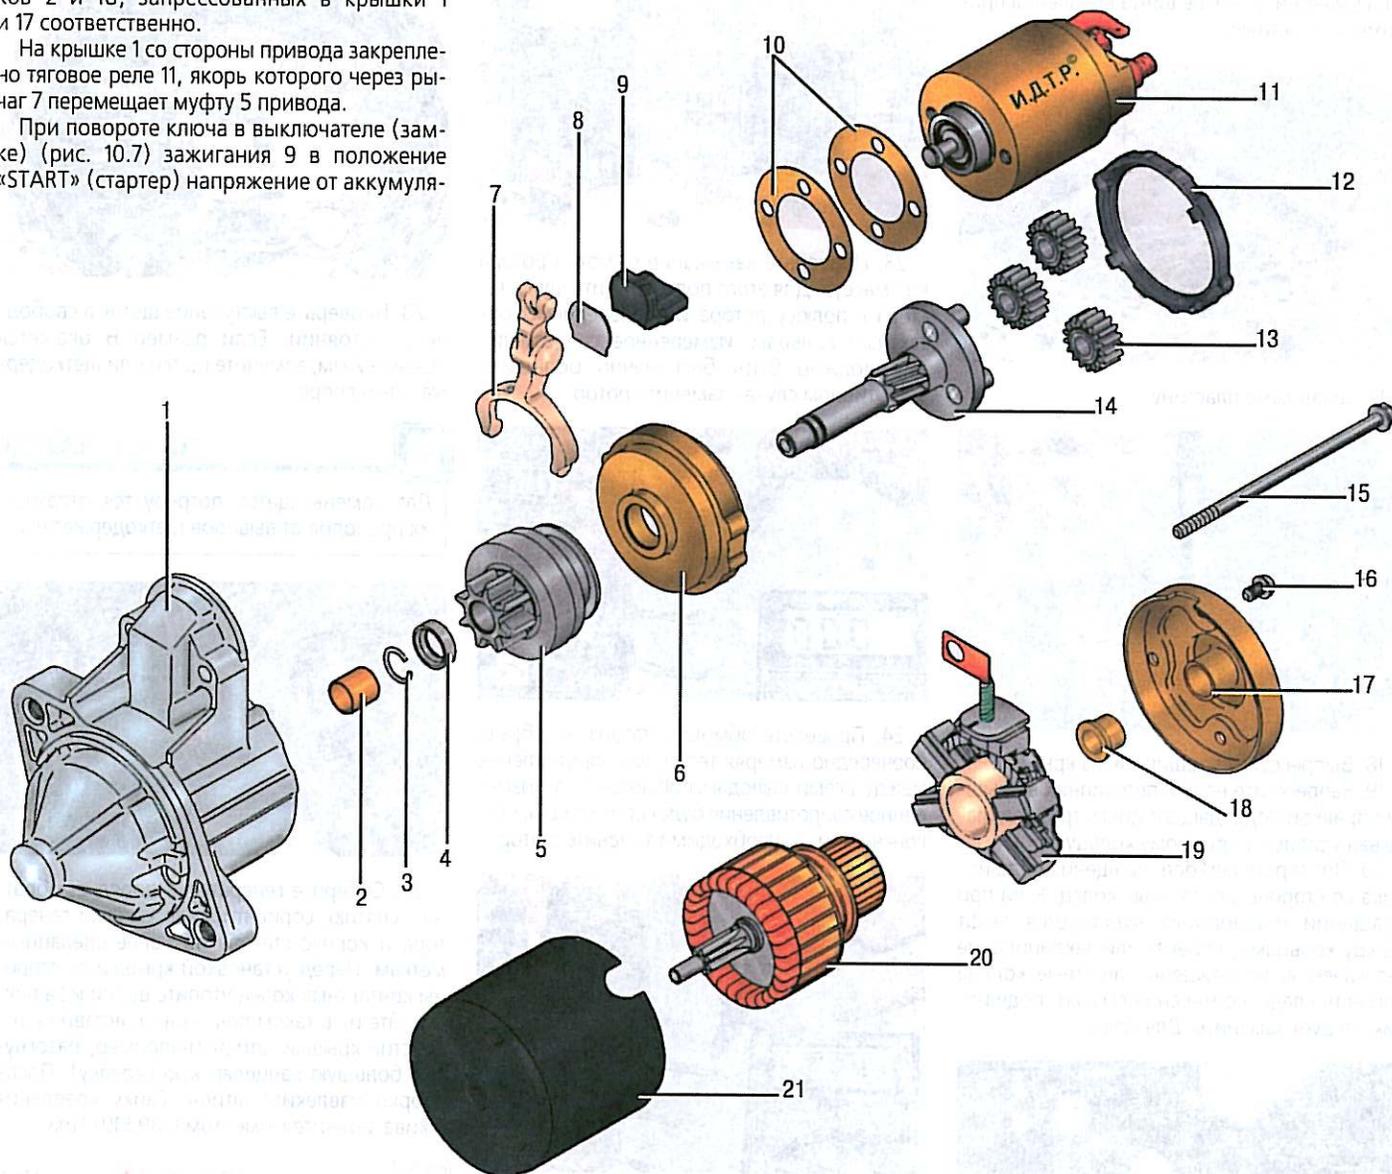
Детали стартера: 1 – крышка со стороны привода; 2, 18 – втулки подшипников; 3 – стопорное кольцо муфты привода; 4 – упорное кольцо муфты привода; 5 – муфта привода; 6 – коронная шестерня планетарного редуктора; 7 – рычаг привода; 8 – накладка опоры рычага привода; 9 – демпфер опоры рычага привода; 10 – регулировочные прокладки; 11 – тяговое реле; 12 – уплотнительное кольцо планетарного редуктора; 13 – планетарная шестерня; 14 – вал привода; 15 – стяжной болт; 16 – винт крепления крышки со стороны коллектора к статору; 17 – крышка со стороны коллектора; 18 – щеткодержатель; 19 – ротор; 20 – статор
